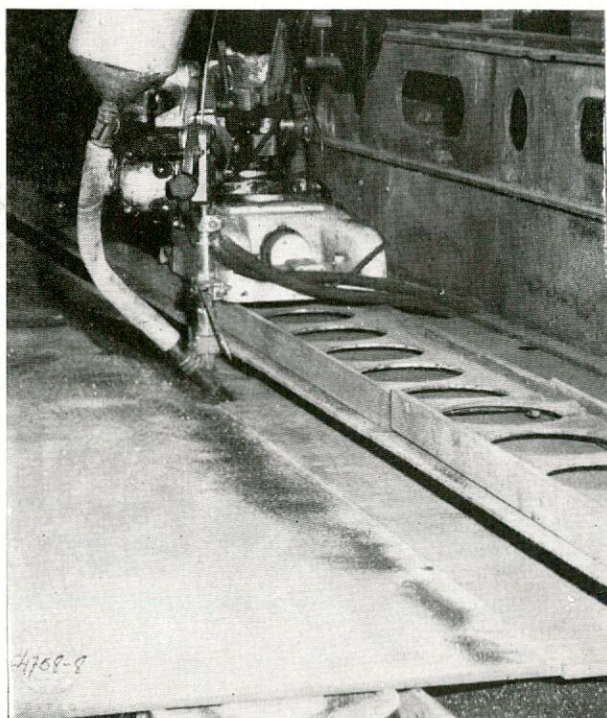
Dispositivo para el montaje y funcionamiento de la máquina de soldar.
